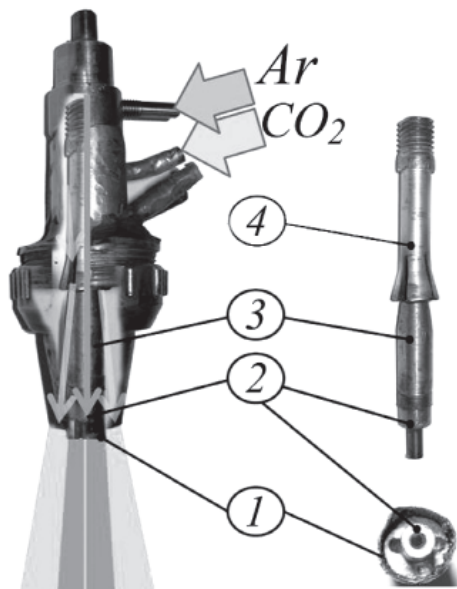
Горелка для комбинированной двухслойной защиты зоны сварки:
